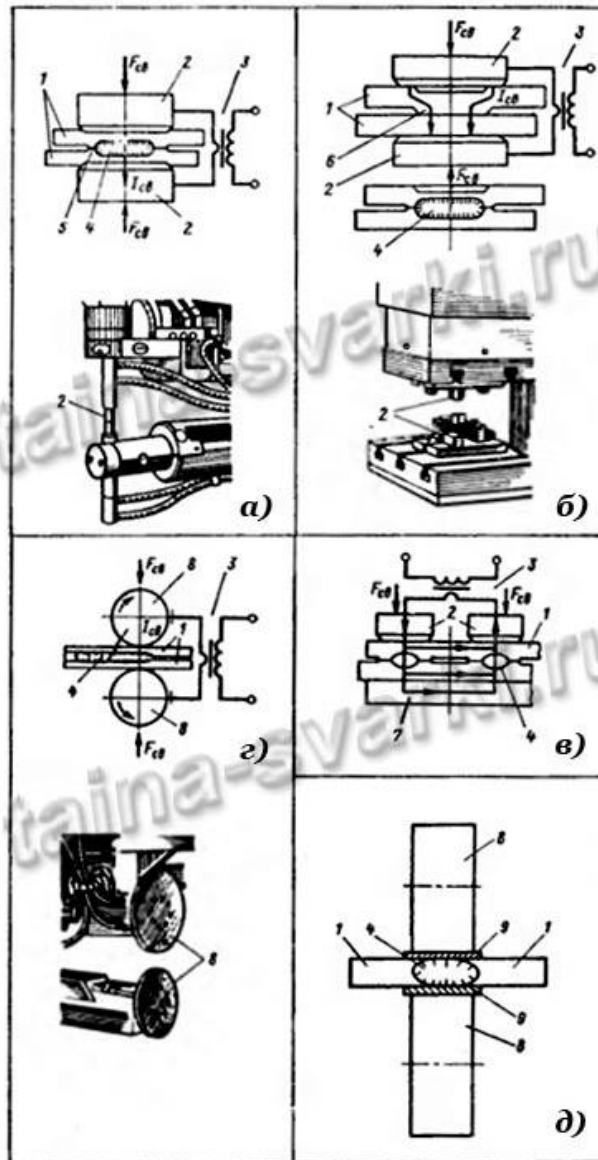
Схеми основних процесів контактного точкового зварювання
